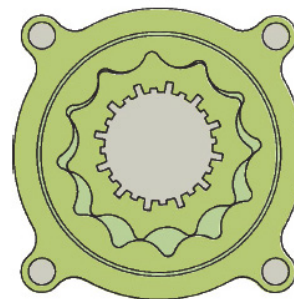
Насос героторного типа приводится в действие от коленчатого вала двигателя; источник: *Pearson Education, Inc.
